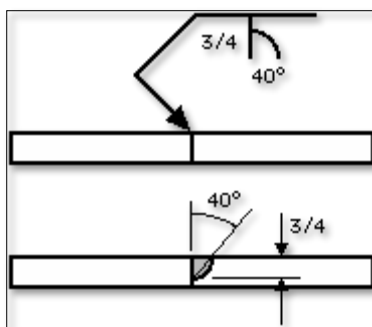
Biselado cóncavo en canal de soldadura.
